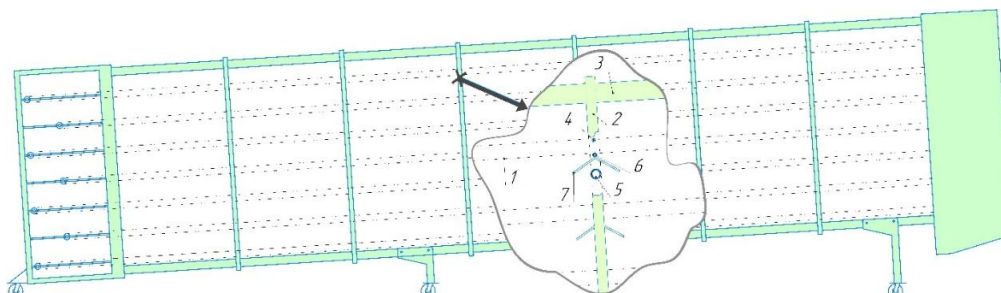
Расположение кварцевых трубчатых электронагревателей в сушилке УСК:
